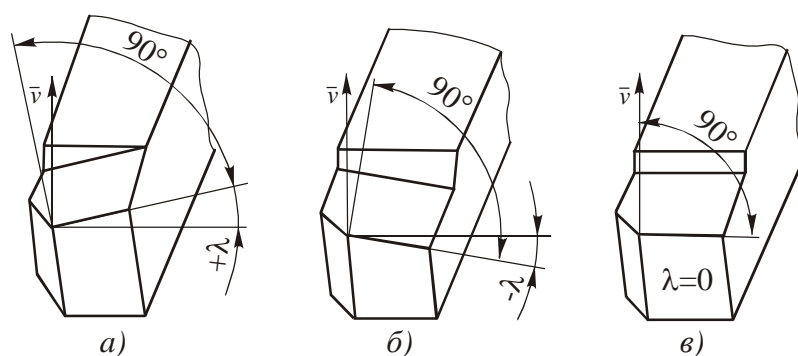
Угол наклона главной режущей кромки λ токарного проходного резца: а - $\lambda > 0$; б - $\lambda < 0$; в - $\lambda = 0$
